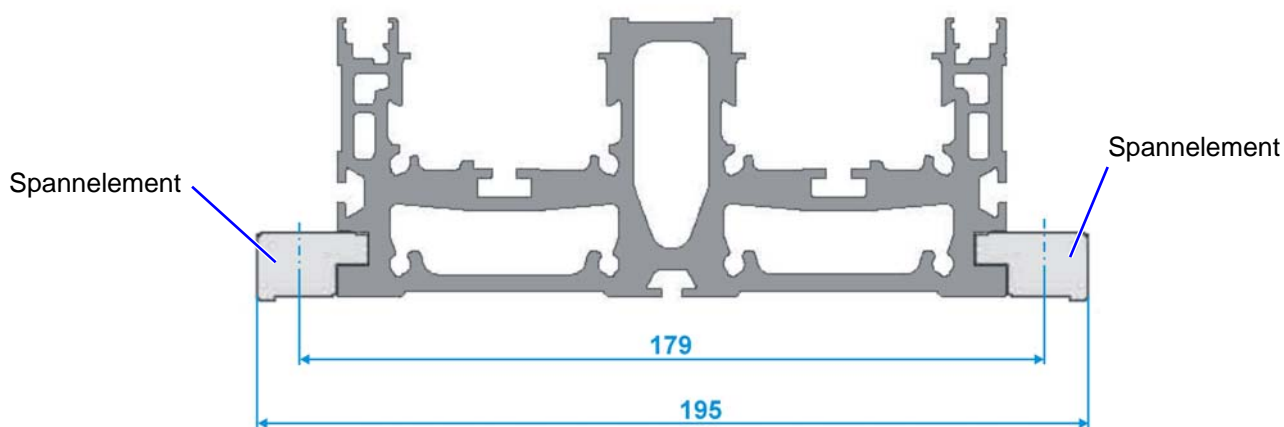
Querschnitt mit Spannelementen und Maßen (Modul 160/15)
